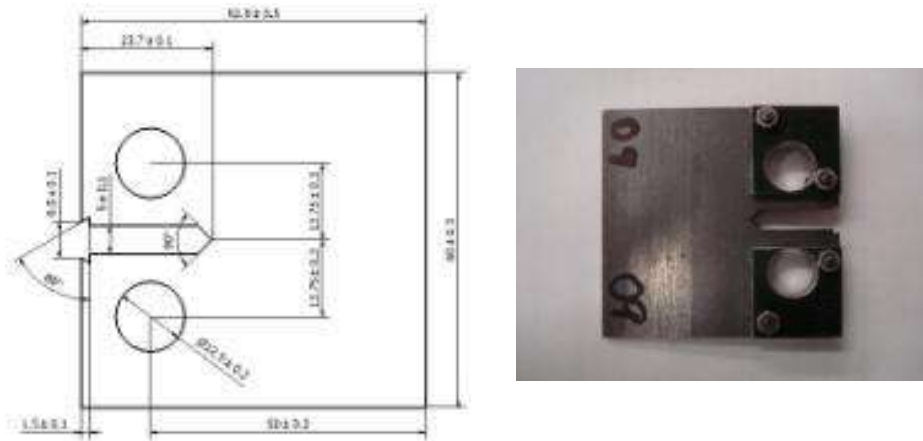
Esquema y probeta para pruebas de fatiga (mecánica de fractura)
